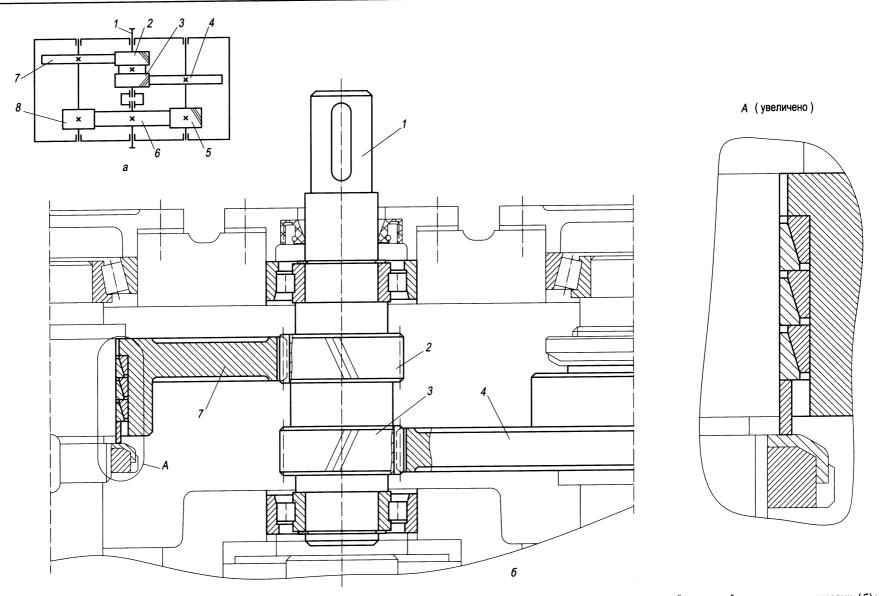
Кинематическая схема цилиндрического двухступенчатого двухпоточного редуктора (a) и эскиз быстроходного вала с шевронной передачей и плавающими опорами (б): 1- вал; 2, 3- шестерни; 4, 7- колеса быстроходной передачи; 5, 8- шестерни тихоходной передачи; 6- колесо тихоходной передачи
